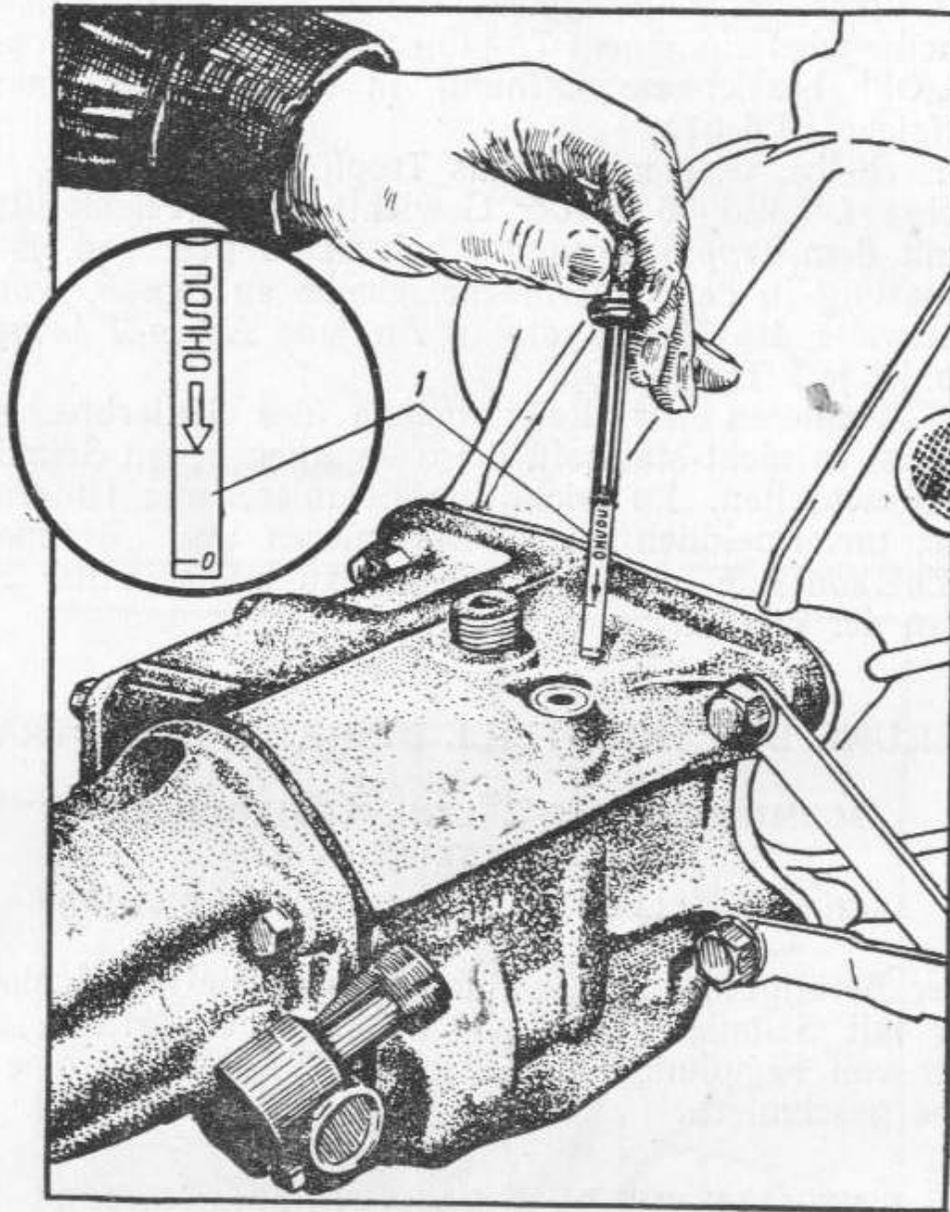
Ölmeßstab für Wechselgetriebegehäuse
